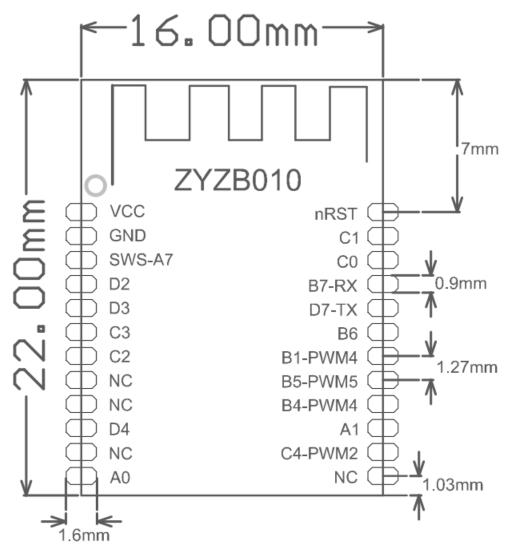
ZYZB010 模组尺寸图 (PCB 厚度 1mm)
